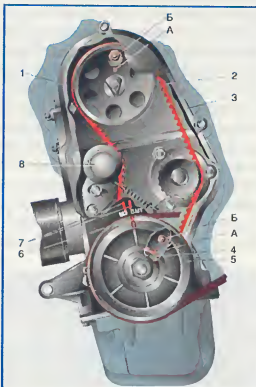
Привод распределительного вала: 1 – наружный защитный кожух зубчатого ремня; 2 – ведомый шкив привода распределительного вала; 3 – зубчатый ремень; 4 – ведущий шкив привода распределительного вала; 5 – шкив привода генератора; 6 – метка на шкиве привода генератора; 7 – метки на наружном кожухе зубчатого ремня; 8 – натяжное устройство.
